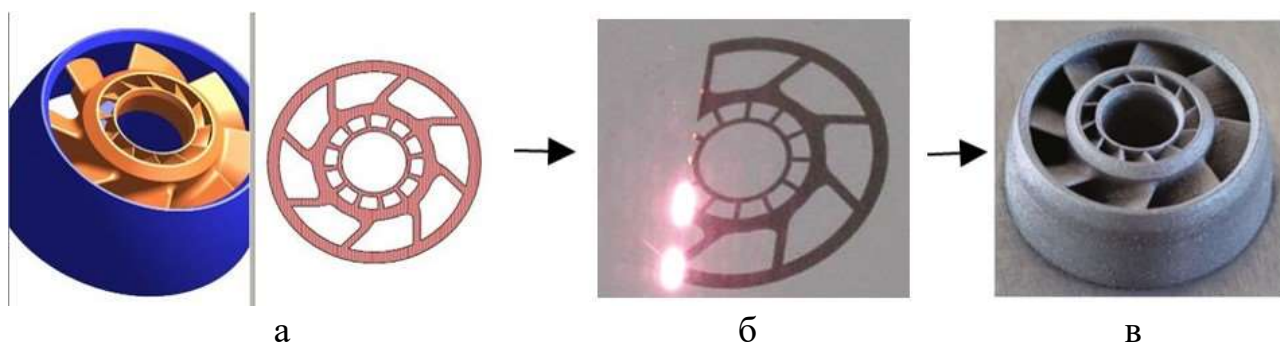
Застосування лазерного порошкового наплавлення для
